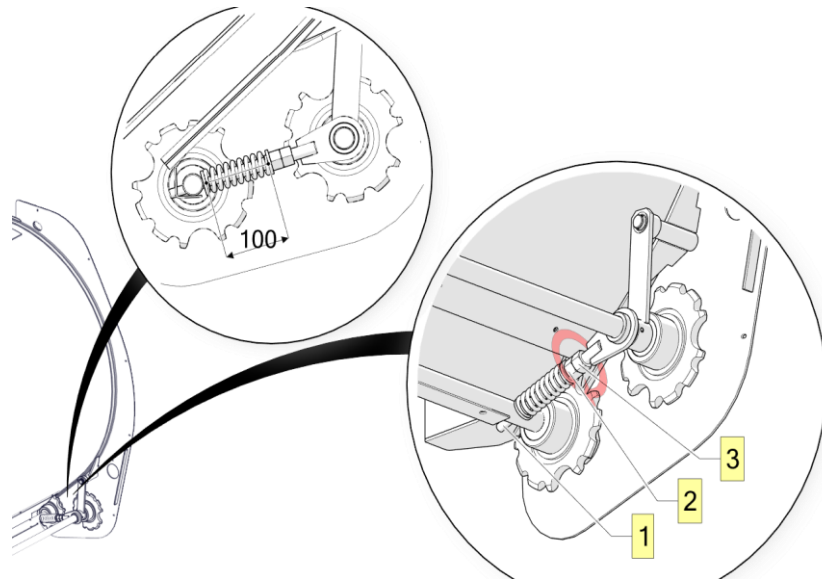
Регулировка натяжения цепно-пруткового транспортера
